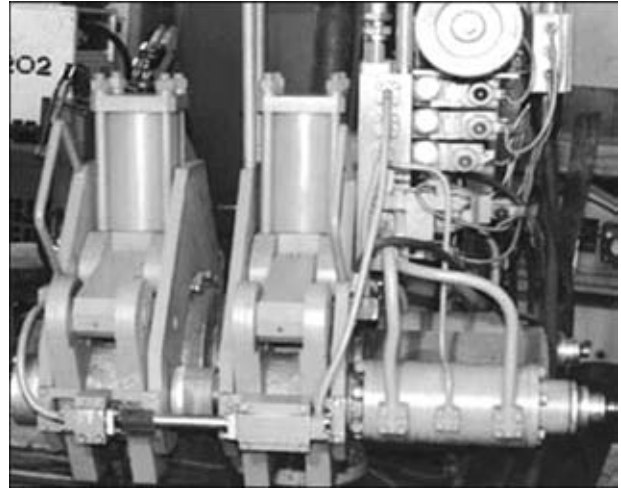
Машина К 872 для прессовой сварки труб диаметром 60...219 мм с нагревом дугой, вращающейся в магнитном поле
